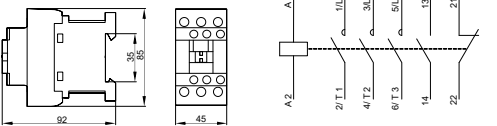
Габаритные размеры контакторов KMI-AL-11812, KMI-AL-22512 / Figure 1 – Overall and mounting dimensions of contactors KMI-AL-11812, KMI-AL-22512
